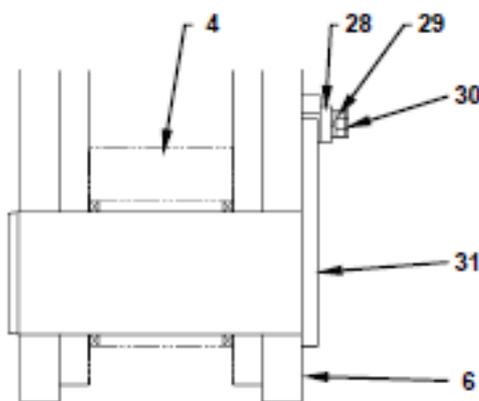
Установка гидроцилиндра рукояти
